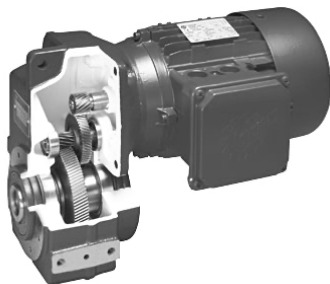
Цилиндрический двухступенчатый мотор-редуктор
